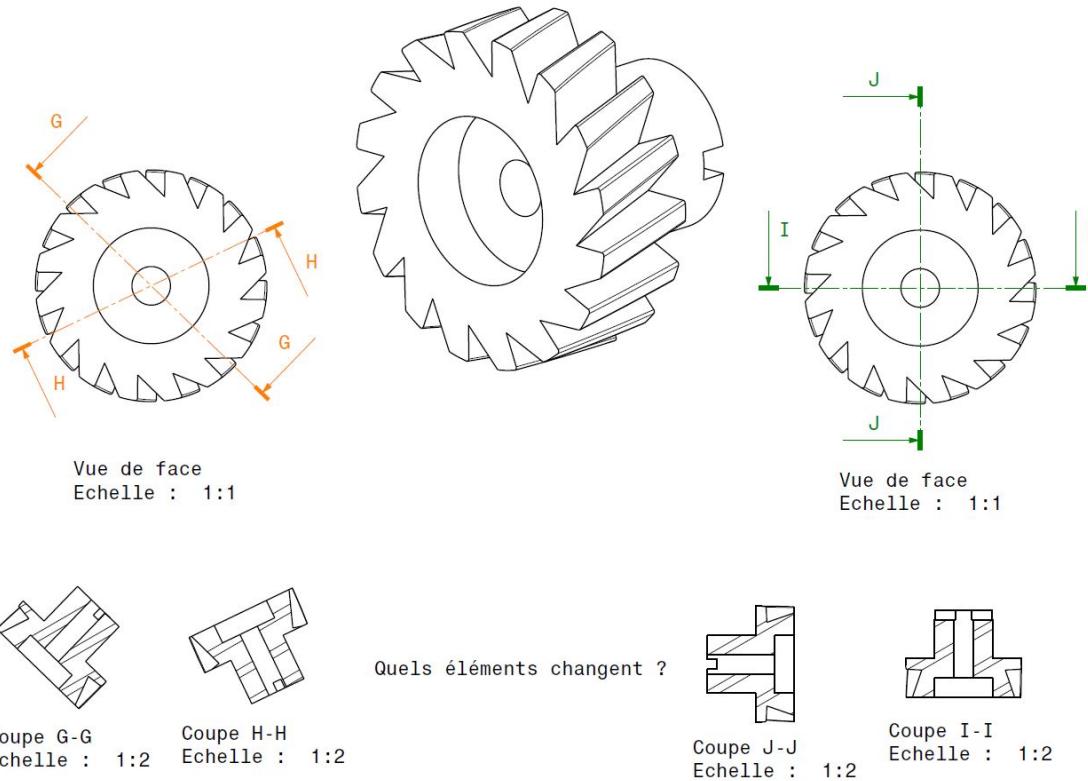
Pièce coupée. A gauche : plans de coupes orienté aléatoirement (coupes G et H). A droite : plans de coupes orienté parallèlement (coupe I) et perpendiculairement (coupe J) à la rainure.
